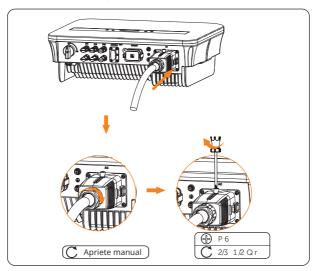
27 Fijación y aseguramiento de la cubierta impermeable de CA
